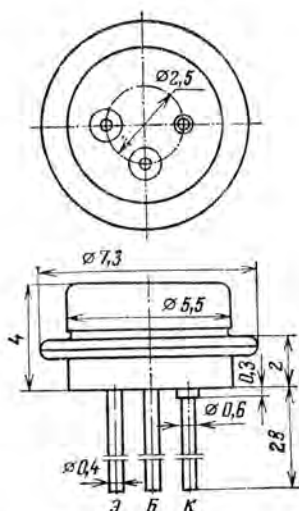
Габаритный чертеж транзисторов КТ306 и КТ316.
